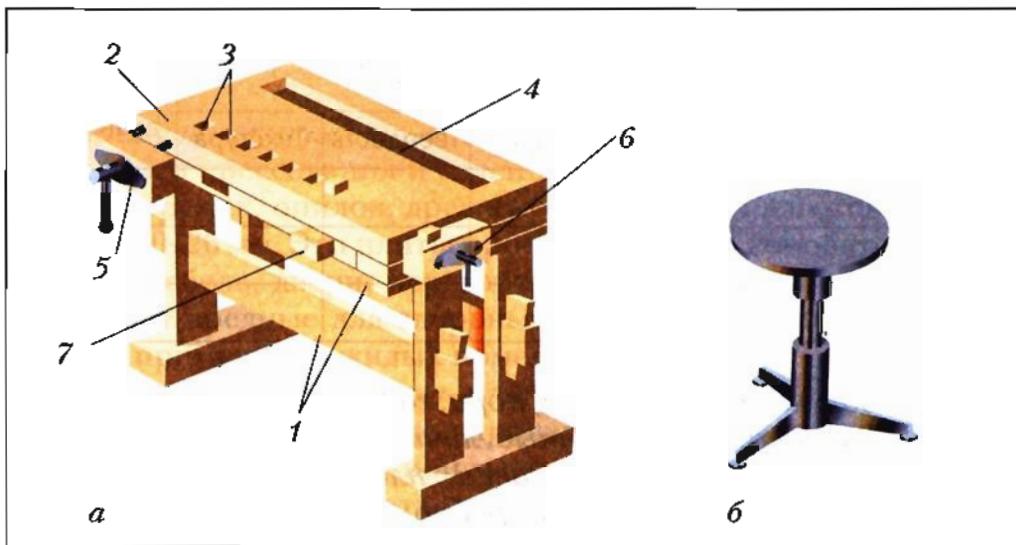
Рабочее место для столярных работ: *а* – столярный верстак (1 – подверстачье, 2 – крышка, 3 – отверстия под клинья, 4 – лоток, 5, 6 – винтовые зажимы, 7 – выдвижная опора); *б* – стул
